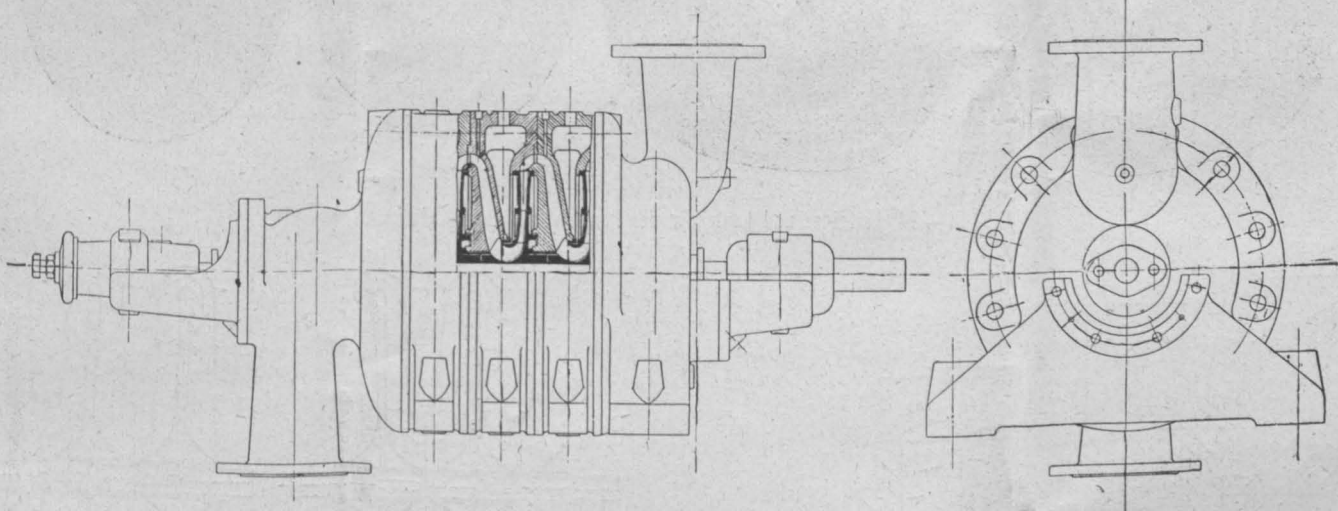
, 28 Pumpe von Ganz & Co. Längenschnitt und Seitenansicht
